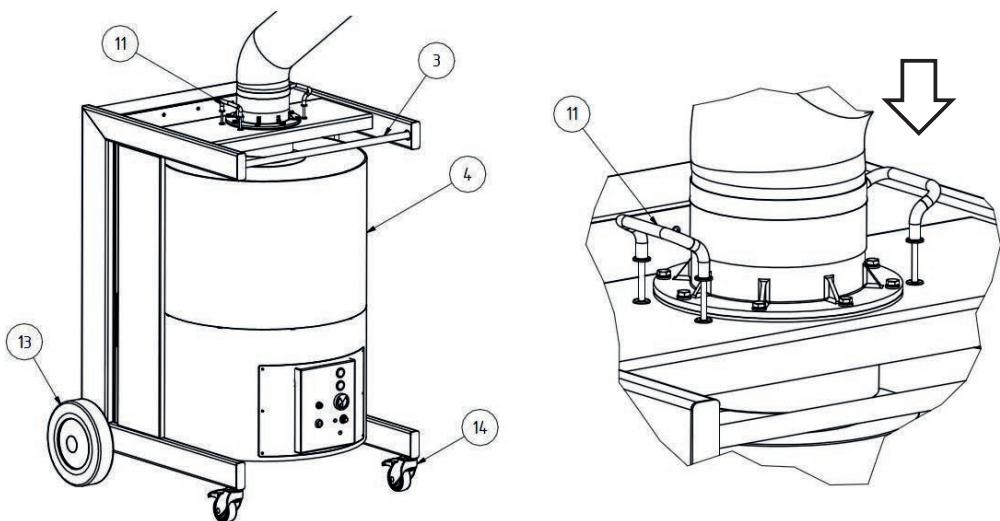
, Rimozione dell'imballaggio e montaggio delle ruote
